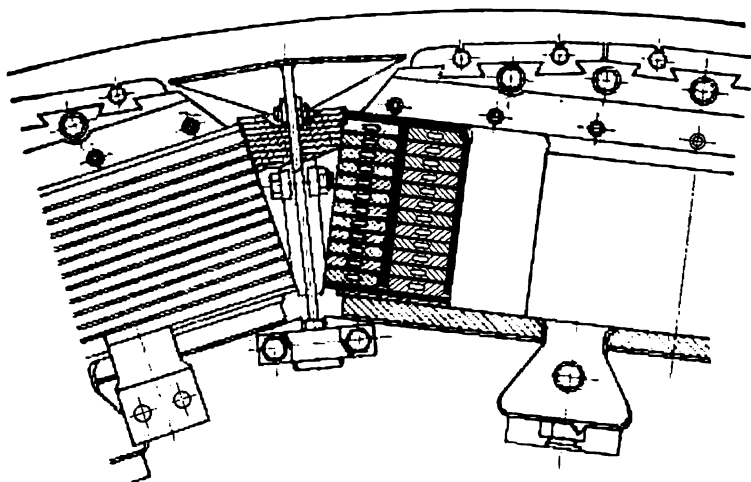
Rotor d'un alternateur hydraulique à refroidissement intérieur de l'enroulement par l'eau.
